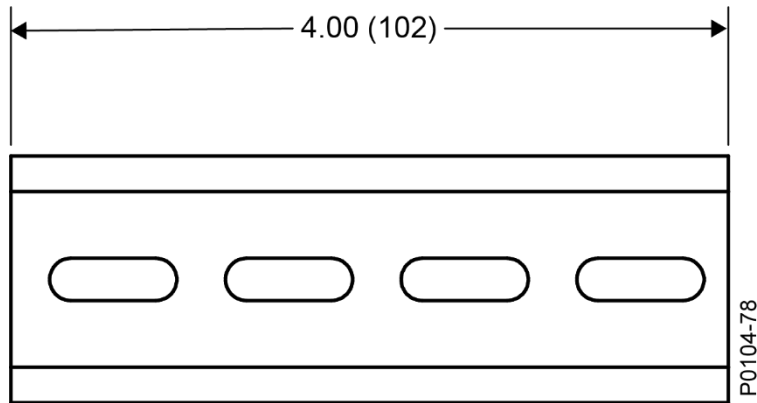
Dimensiones del riel de montaje del conmutador Ethernet y la fuente de alimentación
